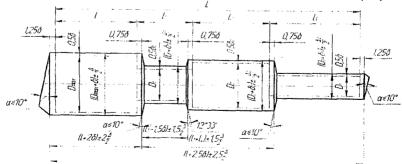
Схема назначения припусков и допусков для поковок 1-ой группы
